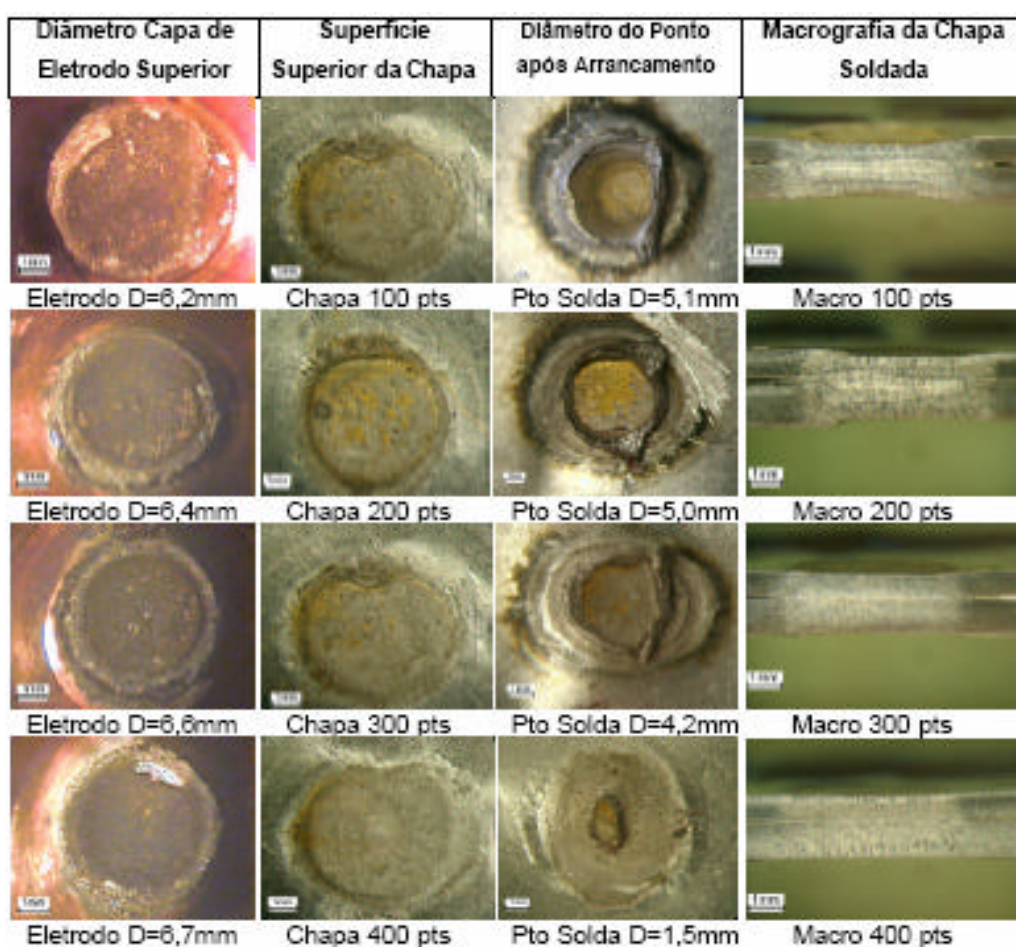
Pontos soldados com a capa de eletrodo A.
